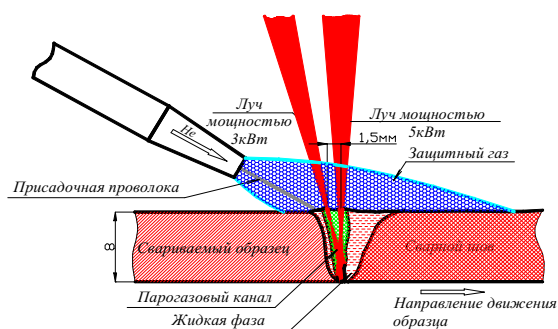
Схема зоны сварки излучениями от двух лазеров.
